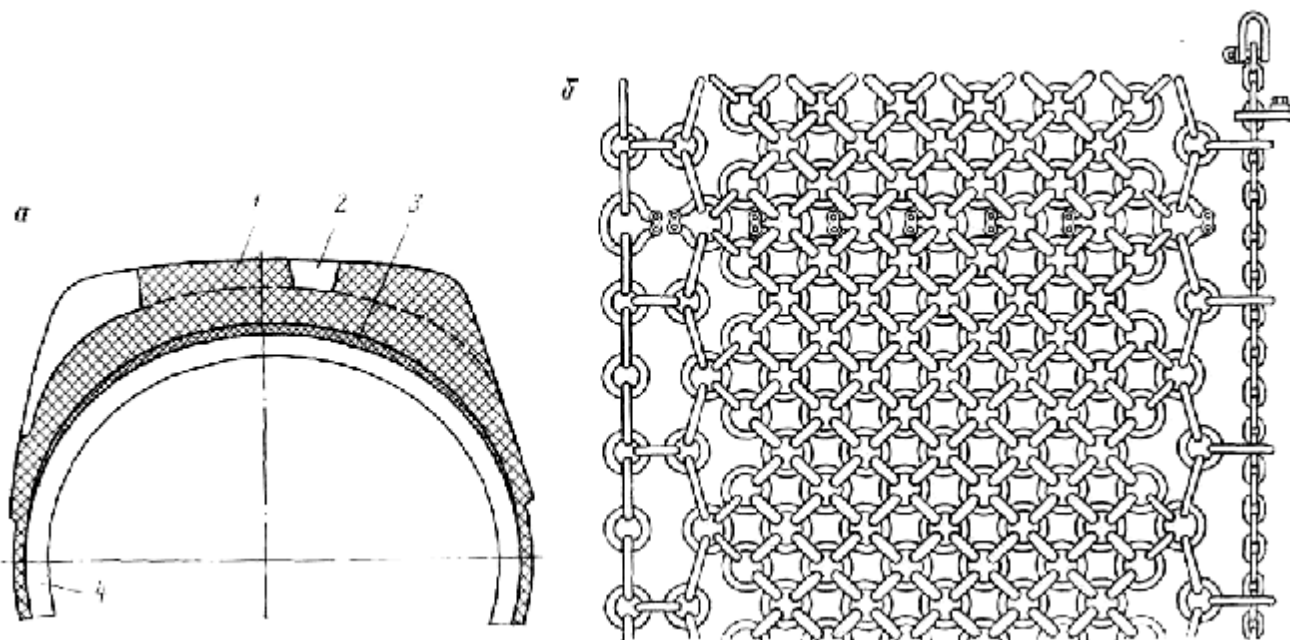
Профиль пневматической шины шахтной самоходной машины (а) и отрезок металлической защитной ленты (б)
